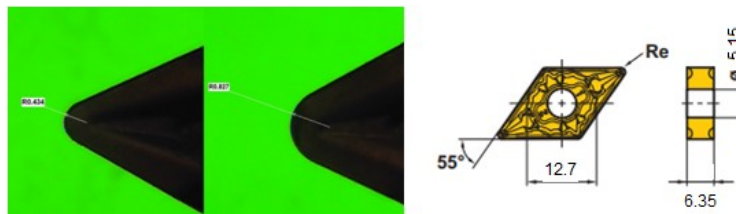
Detalhe da medição dos raios de quina e geometria dos inserts (dimensões em mm)
